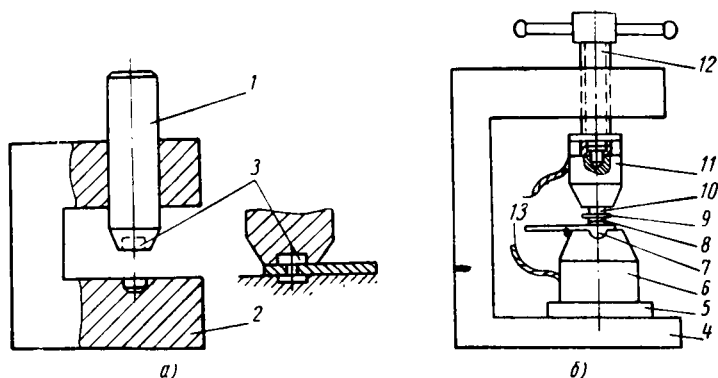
Установка контактов прерывателя и реле-регулятора:
